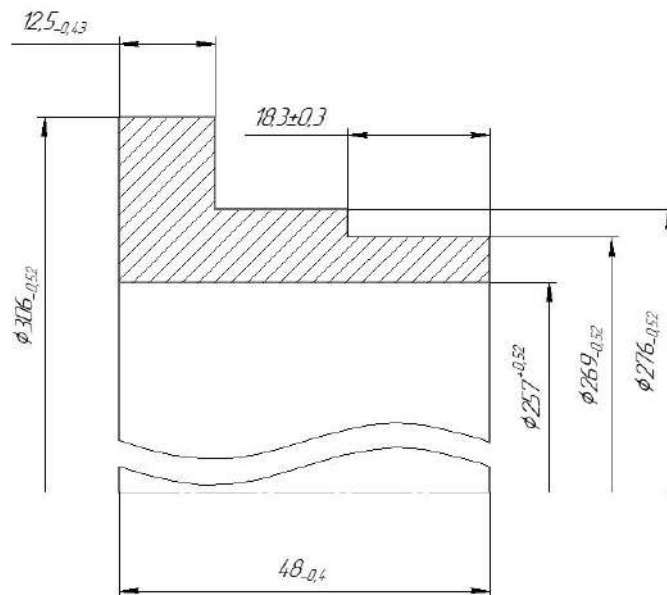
Ескіз вирощуваної заготовки кільця корпусу внутрішнього ТВТ
